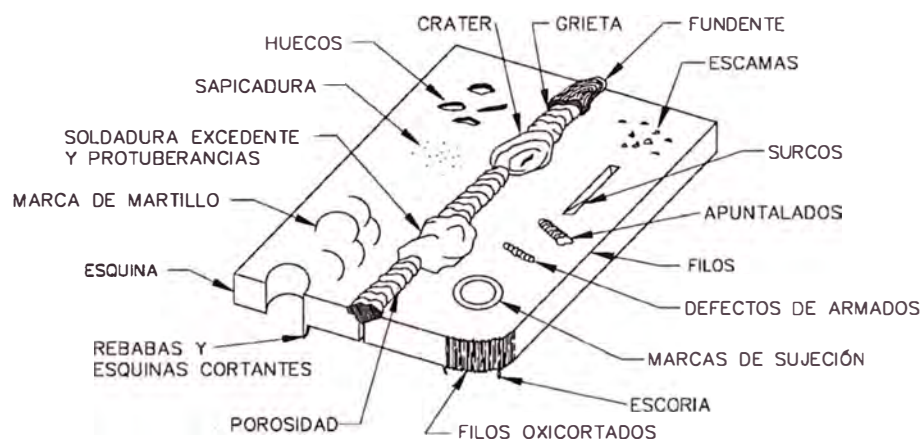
Defectos de Soldadura y Fabricación
